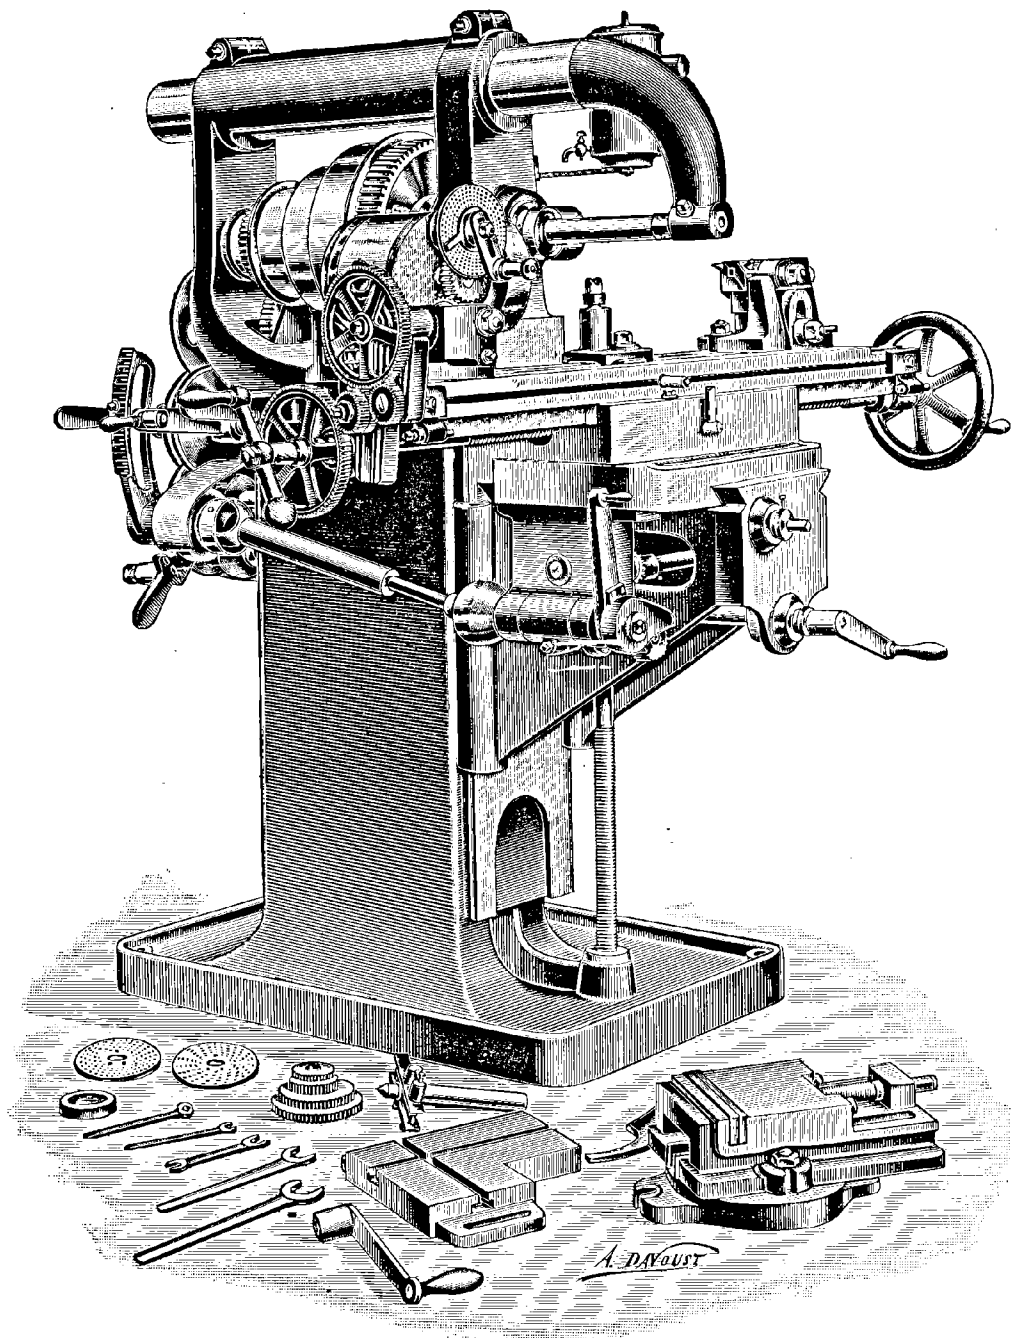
Machine à fraiser de Kemp Smith disposée pour fraiser horizontalement.
